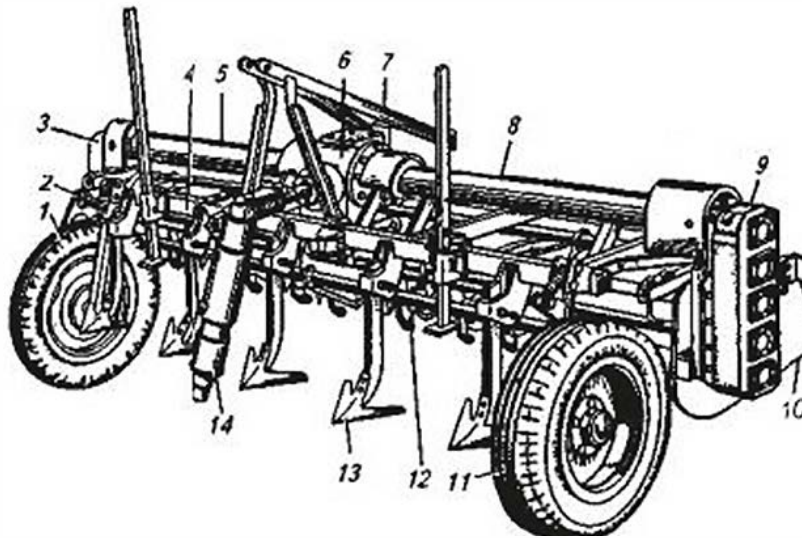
Культиватор фрезерний КФГ-3,6:
